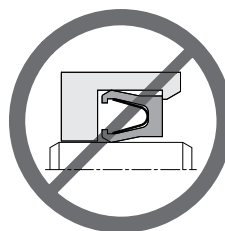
Неправильная установка ступенчатой посадочной канавки
